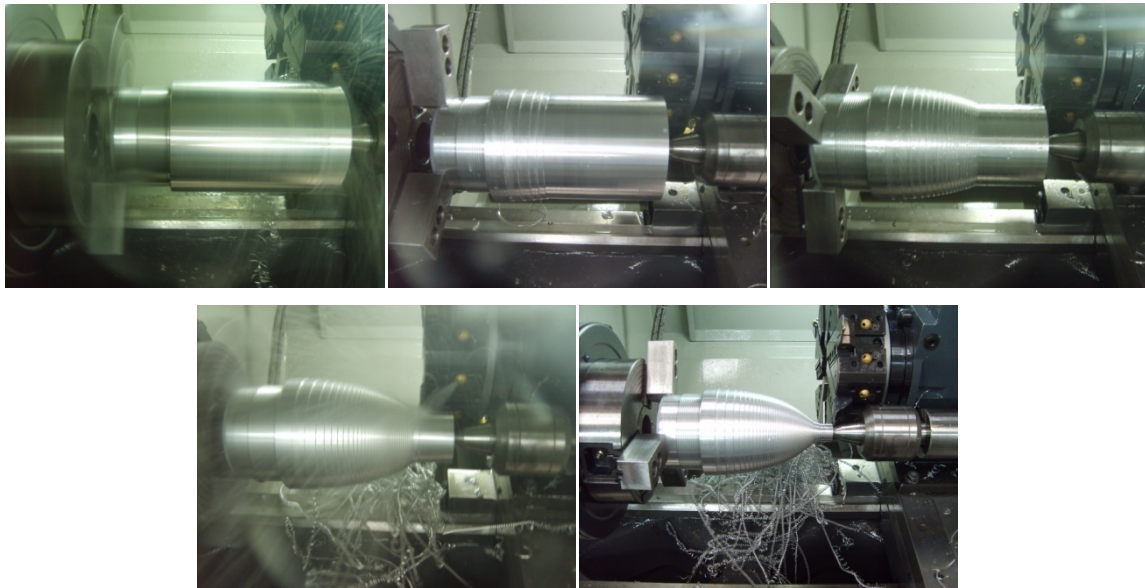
Processo de usinagem no torno CNC do nariz do penetrômetro
